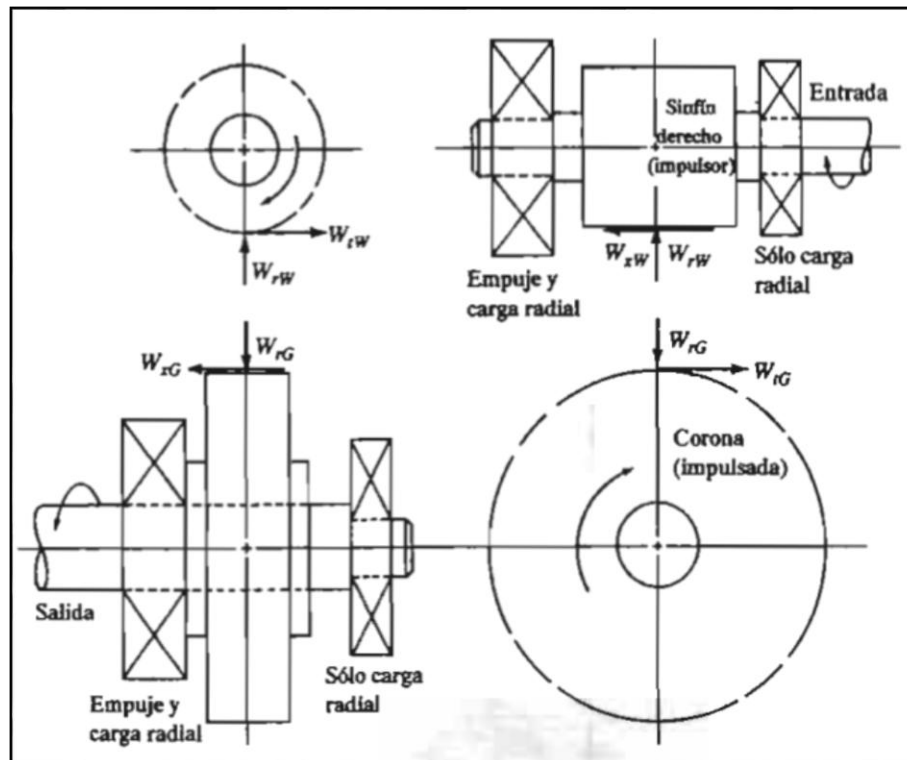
Fuerzas sobre tornillo sinfín y rueda dentada.
